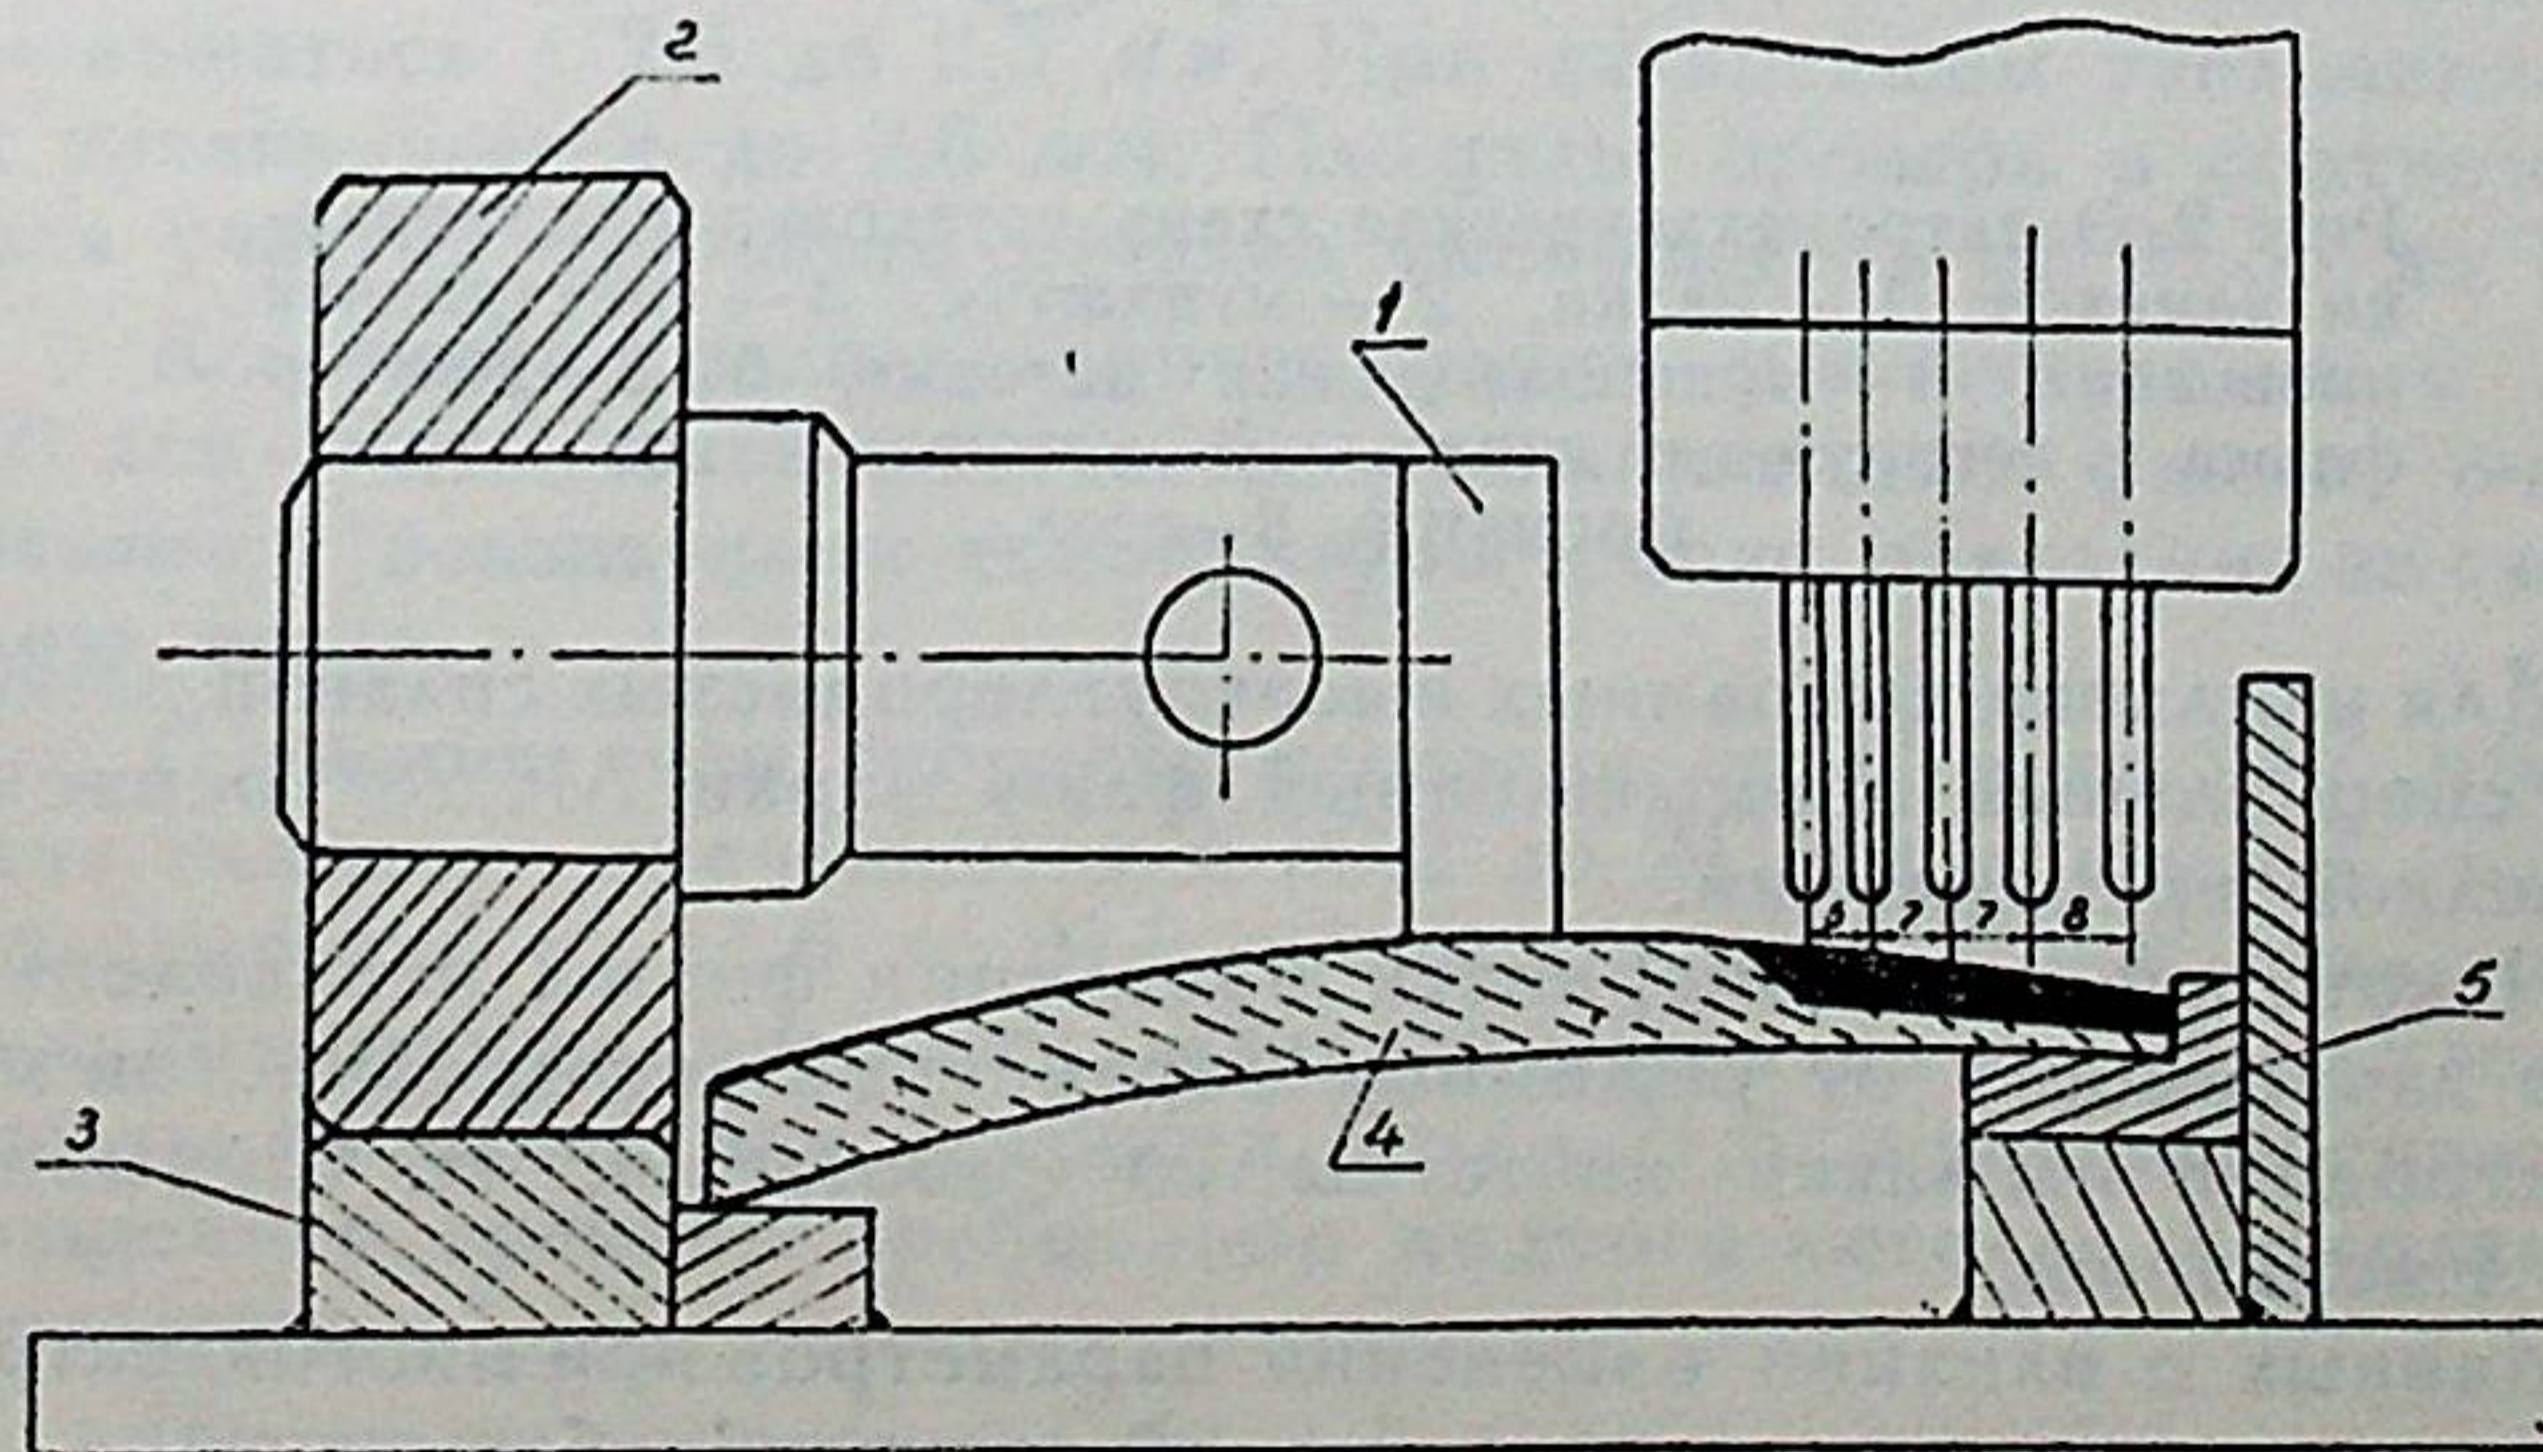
Схема крепления лемеха в наплавочном кондукторе: 1—эксцентрик, 2—втулка, 3—пластина, 4—лемех, 5—медная пластина.
